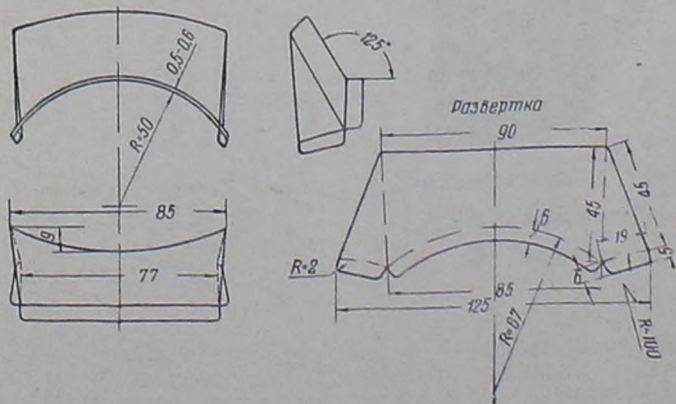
Приспособление для маскировки освещения номерного знака автомашины М-1:
